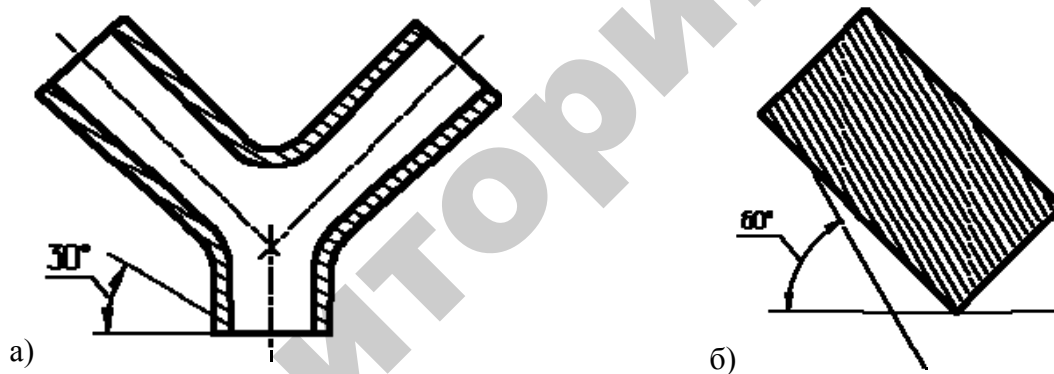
Штриховка под углом 30° к рамке чертежа
